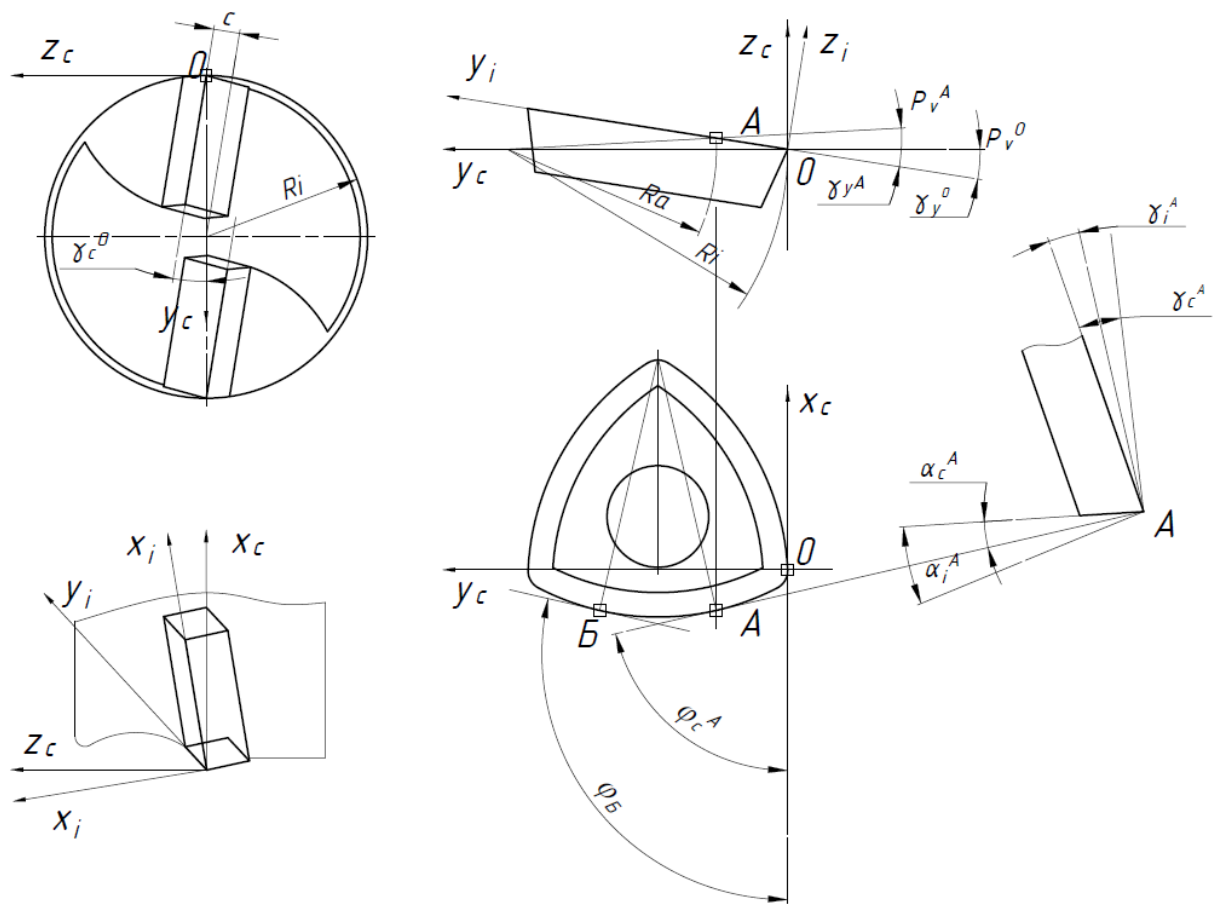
Розрахункові схеми для збірного свердла: а – кути орієнтації ЗТП у корпусі свердла; б – статичні геометричні параметри
